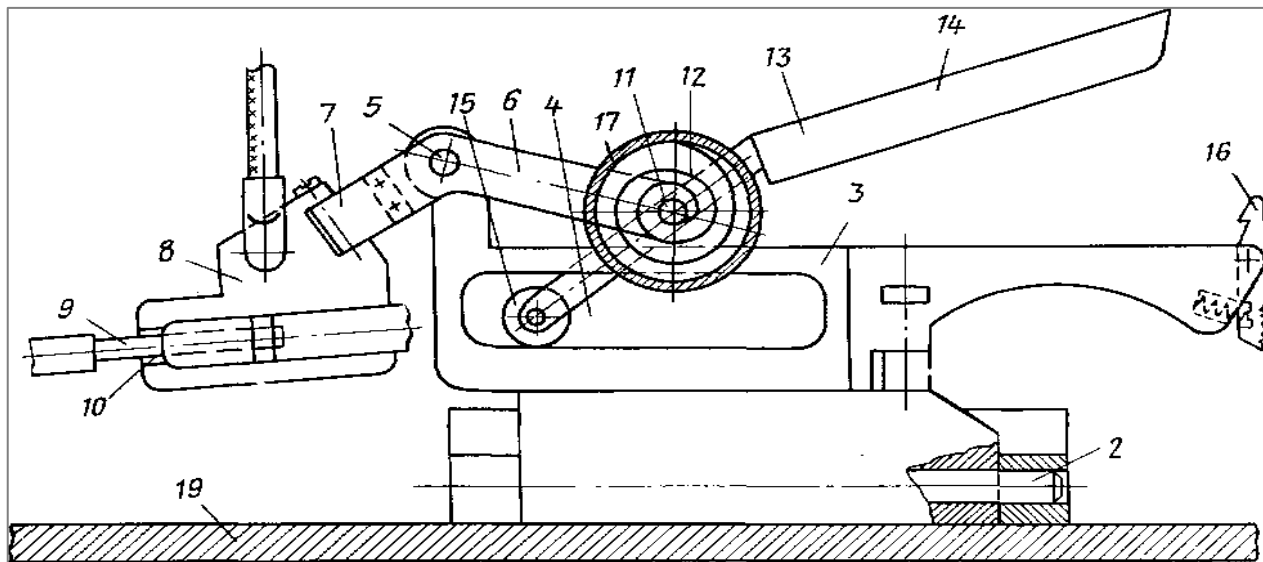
, а – Устройство для сварки наклонным электродом вид сбоку
